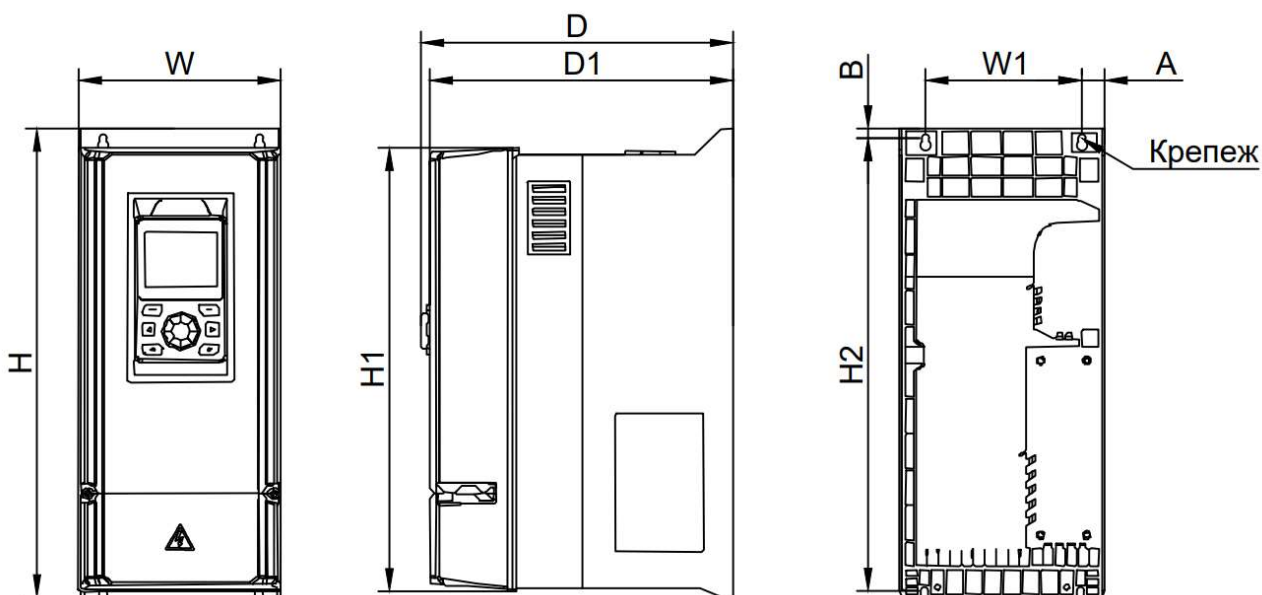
Чертеж преобразователя частоты типоразмеров M1-M3
